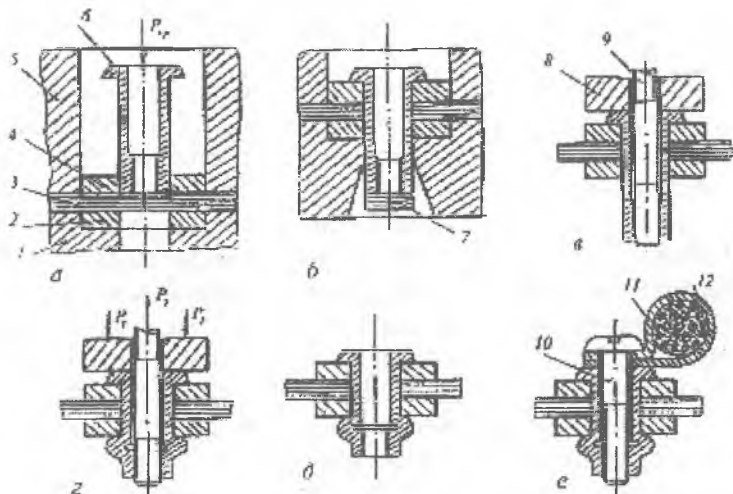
Процесс образования соединения заклепками типа гайка-пистон:
